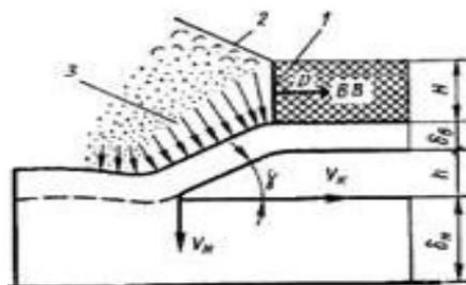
Схема установившегося процесса сварки взрывом:
